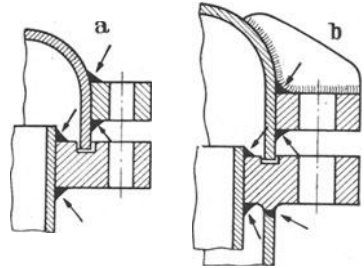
Deckelschweißungen bei Dampfgefäßverschlüssen.
